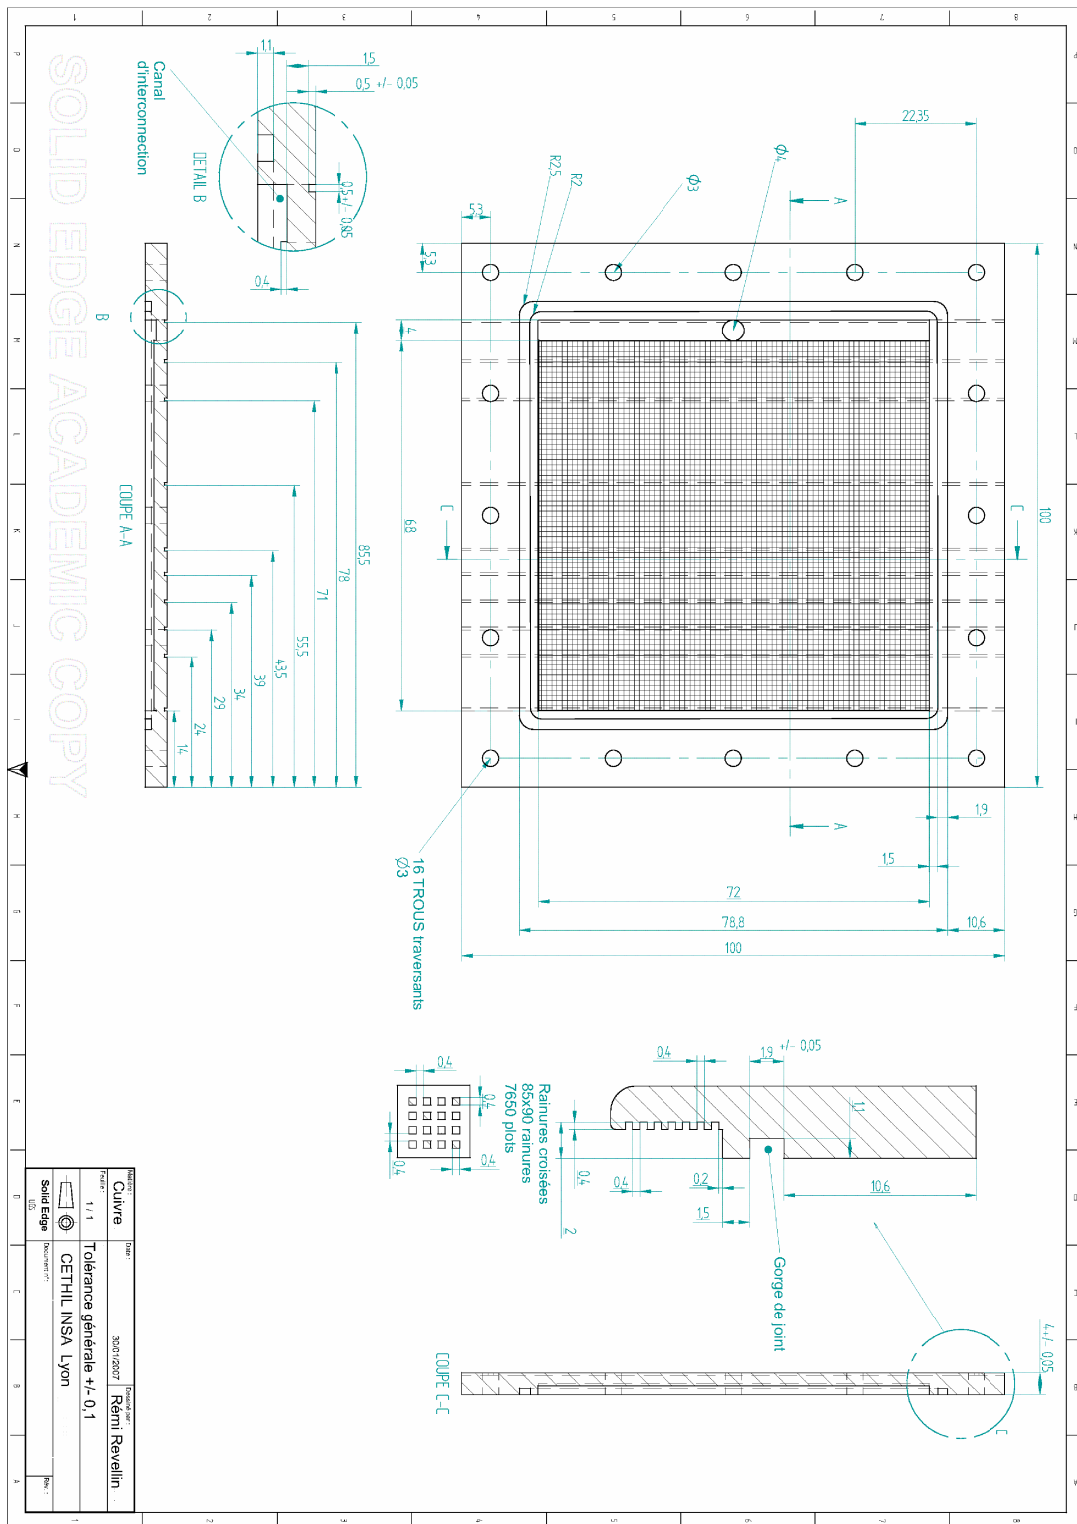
Plan du DTD en cuivre à rainures croisées
